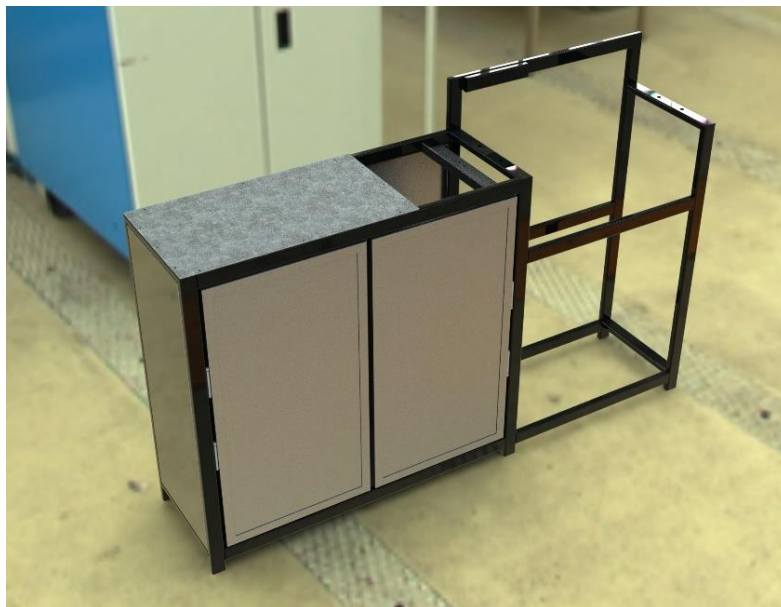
Bastidor cubierto con plancha de acero galvanizado.
